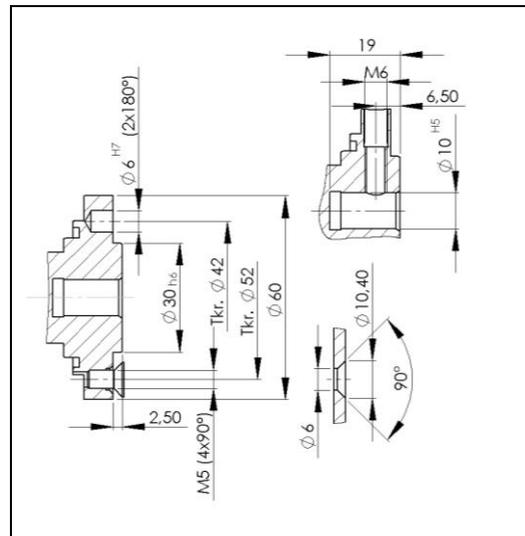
Werkzeugaufnahme Teilkreis 52mm
